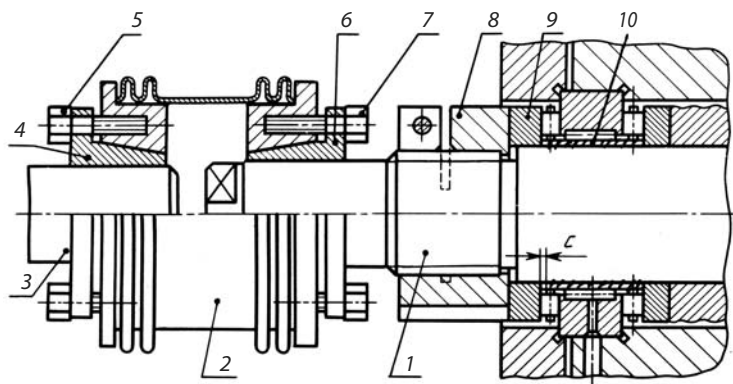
Конструкция соединительной муфты и опоры ходового винта
